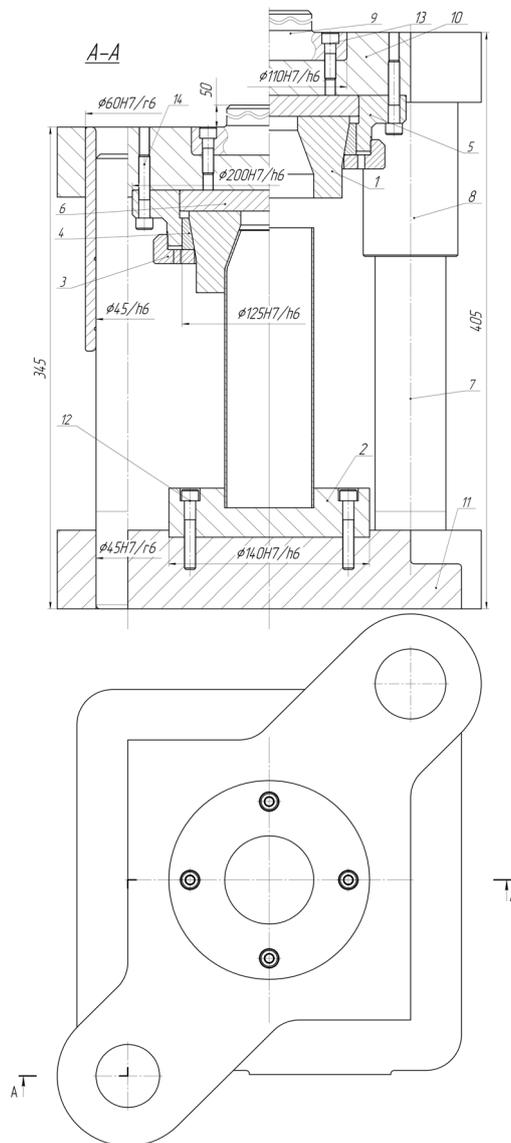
Універсальний штамп для обтиску трубчатих заготовок
